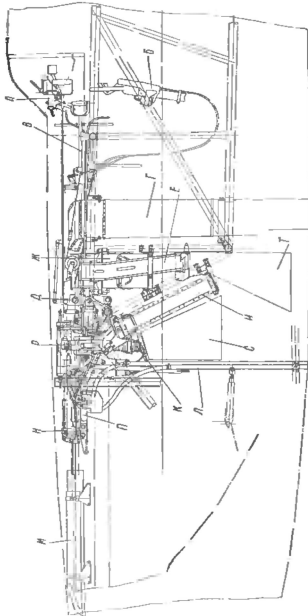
Общий вид стрелковой установки (вид сбоку).
